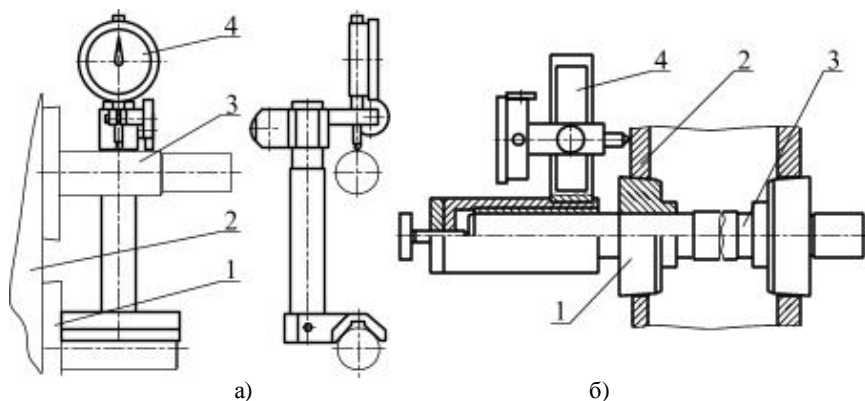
Пристрій для контролю паралельності (а) та перпендикулярності (б) осей корпусних деталей: 1 – конічна втулка; 2 – корпусна деталь; 3 – оправка; 4 – вимірювач з індикатором
